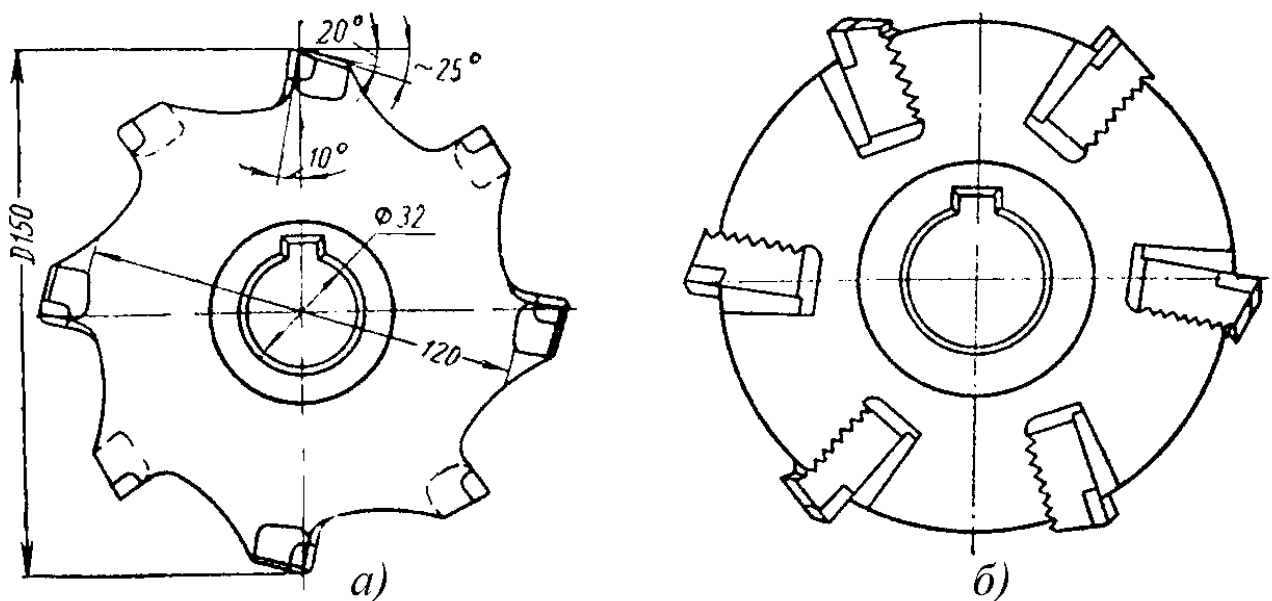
Дисковая фреза: а - с напаянными твердосплавными пластинами; б - со вставными зубьям.
